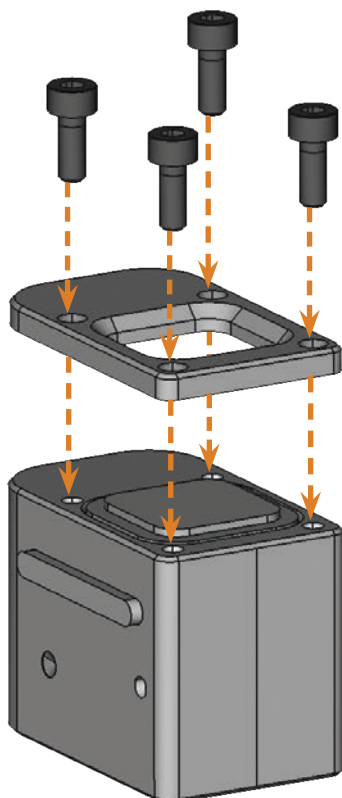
REMONTER LE MAGASIN D'OUTILS
